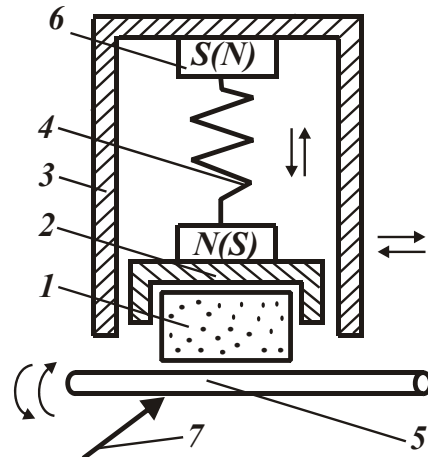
Устройство для магнито-импульсного шлифования с односторонним расположением электромагнитных систем: 1 – шлифовальный круг; 2 – патрон для шлифовального круга с электромагнитом; 3 – направляющий цилиндр, по которому перемещается патрон со шлифовальным кругом; 4 – пружина подвески патрона со шлифовальным кругом; 5 – обрабатываемая деталь; 6 – электромагнит; 7 – лазерный луч контроля размеров обрабатываемой детали.
